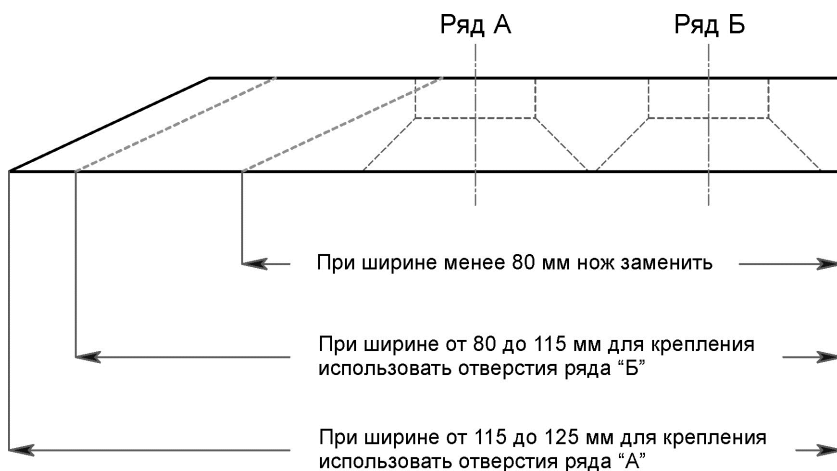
Выбор ряда отверстий для крепления ледового ножа
